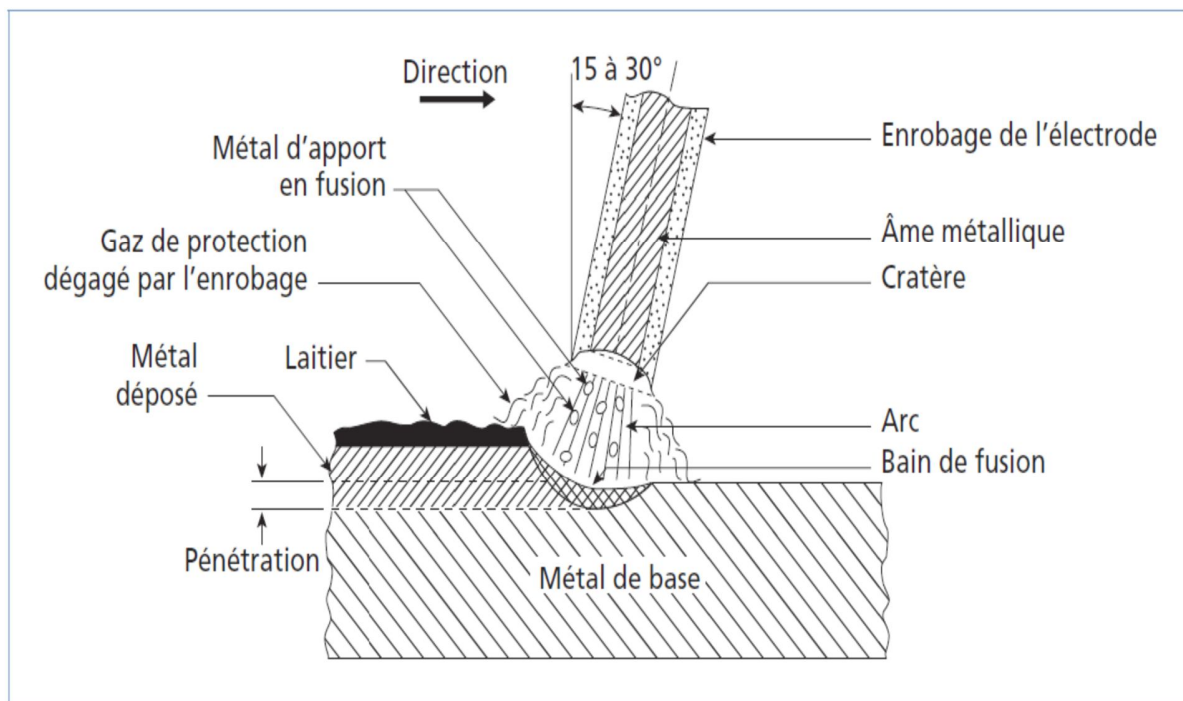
Principe de soudage à l'arc avec électrode enrobée (SMAW). [16]
